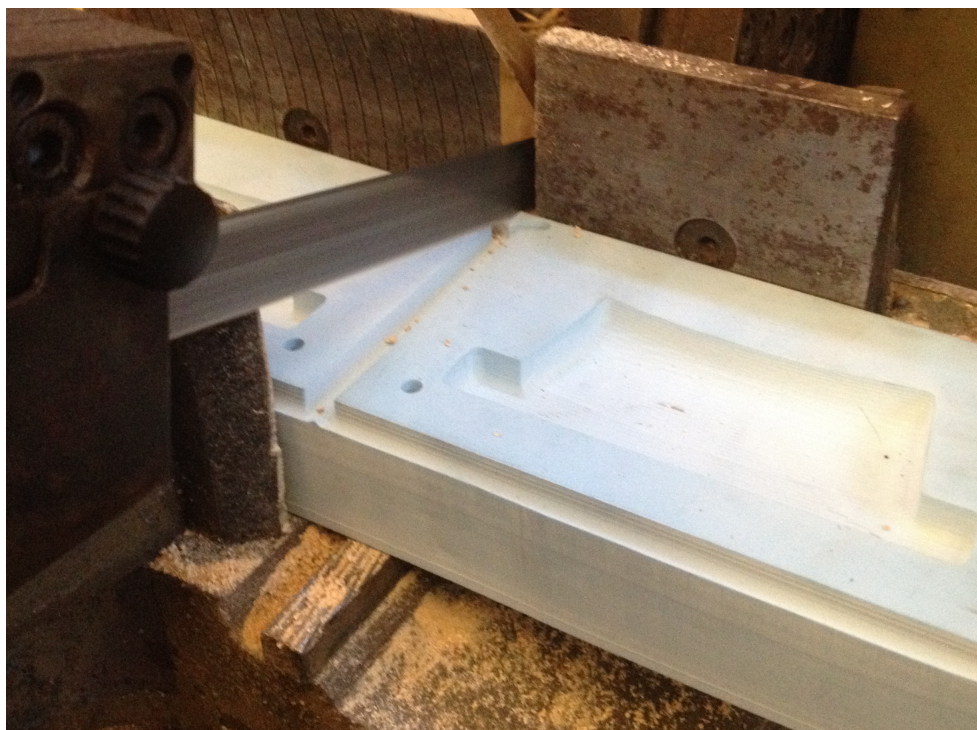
Preparación del Molde. Corte del tocho donde están las dos partes del molde. (Fuente: Propia)
